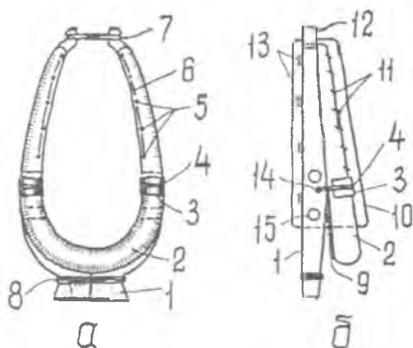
Крепление хомутины и подушки к клещам: а - клещи и хомутина в сборе (вид сзади); б - клещи, хомутина и подушка в сборе (вид сбоку): 1 - клещи; 2 - хомутина; 3 - подкладка под бечевку; 4 - бечевка; 5 - гвозди; 6 - сыромятный ремешок; 7 - стойный ремень; 8 - супонь; 9 - шов хомутины; 10 - хомутная подушка; 11 - шов, соединяющий подушку и хомутину; 12 - ремень на верхние рожки клещей; 13 - крепление сшивкой подушки к клещам спереди; 14 - отверстие для бечевки; 15 - гужевое отверстие
